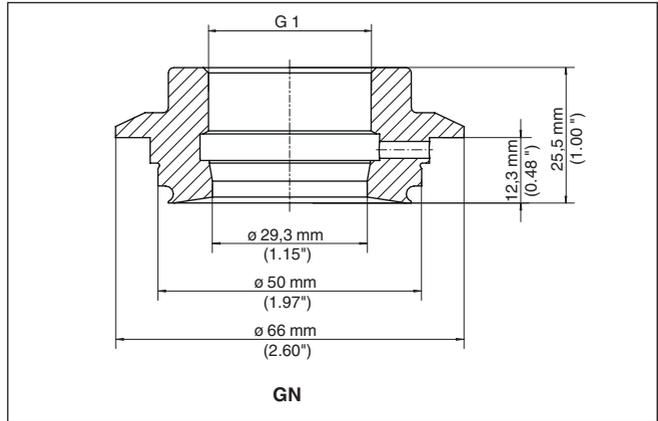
Dimensiones adaptador de rosca G1 (DIN 3852-X) a Varivent forma F 25
